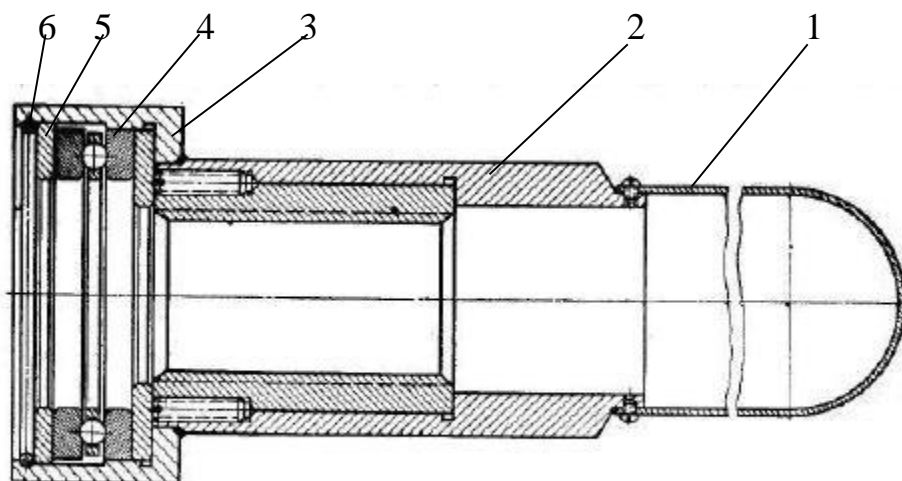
Зажимной механизм: 1- колпачок; 2 – гайка; 3 – корпус подшипника; 4 – радиальный подшипник; 5 – стопорное кольцо; 6 – пружинное кольцо
